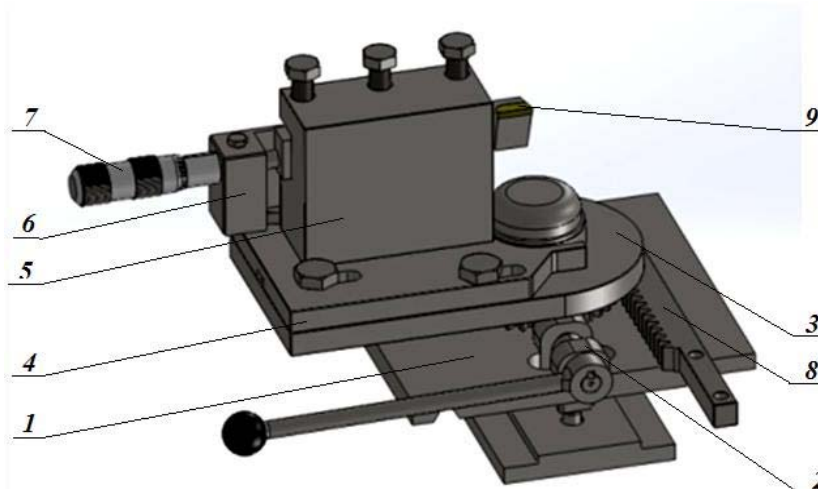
Поворотний пристрій для токарної обробки неповних сферичних поверхонь:
